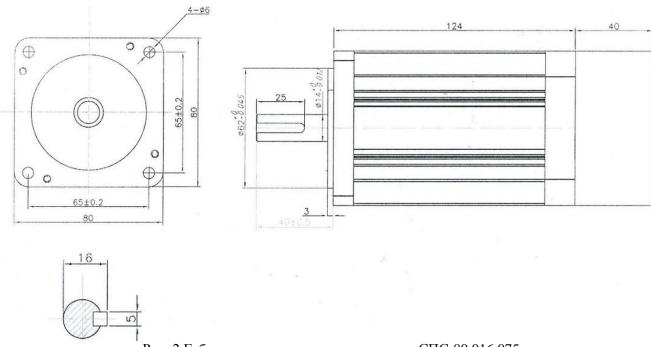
Габаритные размеры серводвигателя СПС-80.016.075
